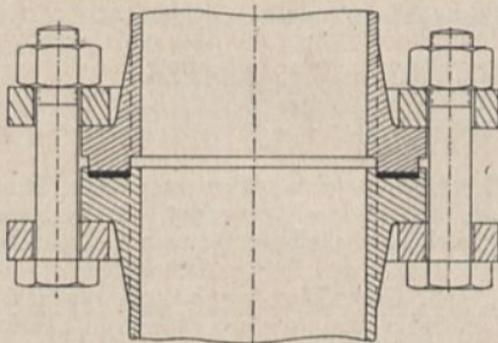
Flanschverbindung mit aufgeschweißten Bordringen mit Nut und Feder und losen Flanschen.
